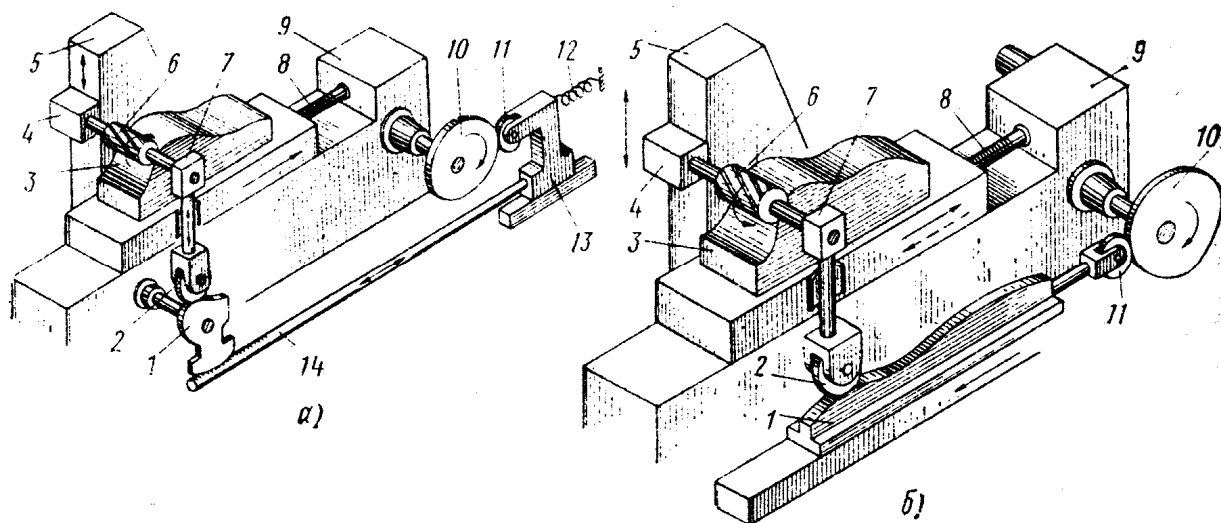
Схемы фрезерования пуансона штампа для гибки
